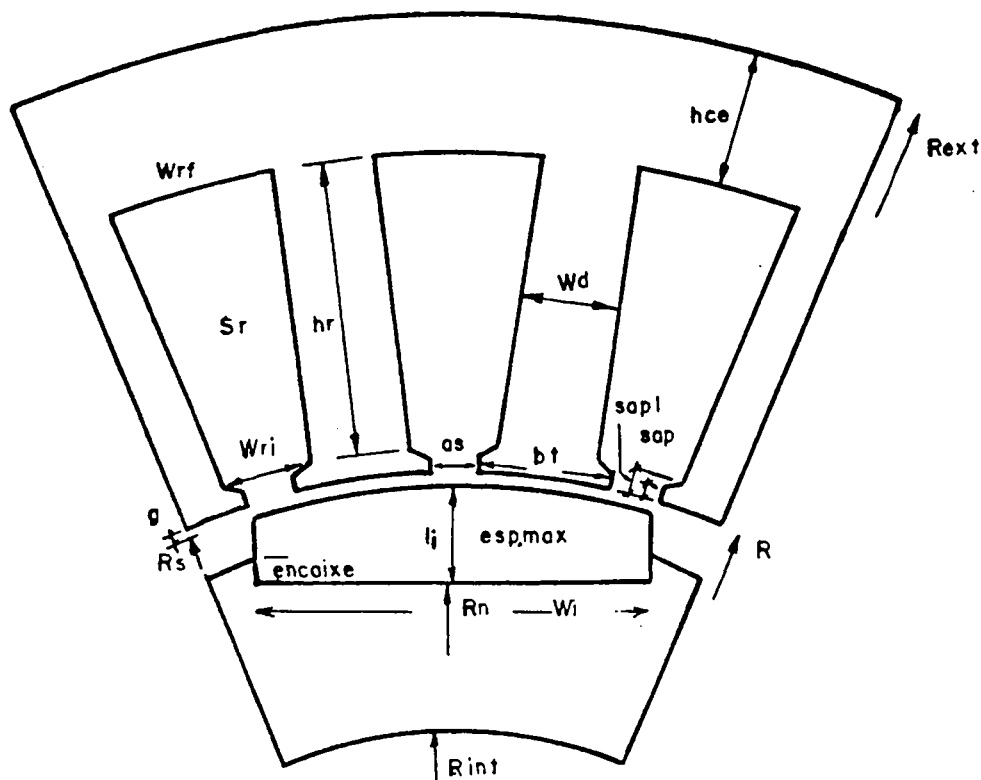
Definição das dimensões dos pacotes magnéticos
